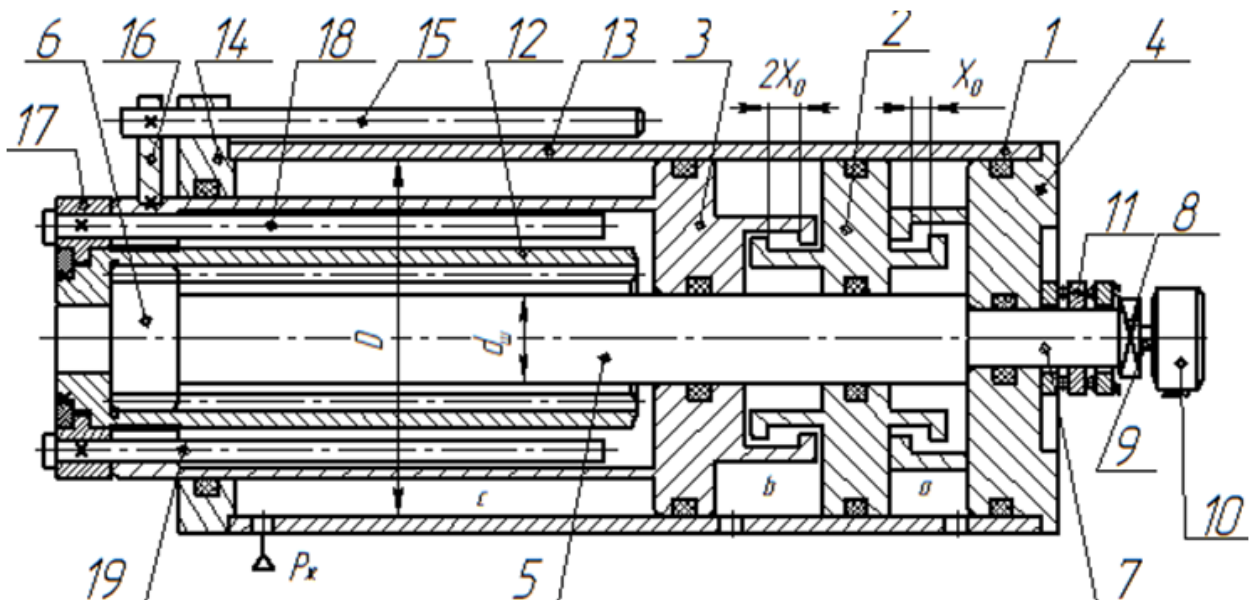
Багатопозиційний пневмоелектричний привод руки промислового робота.
